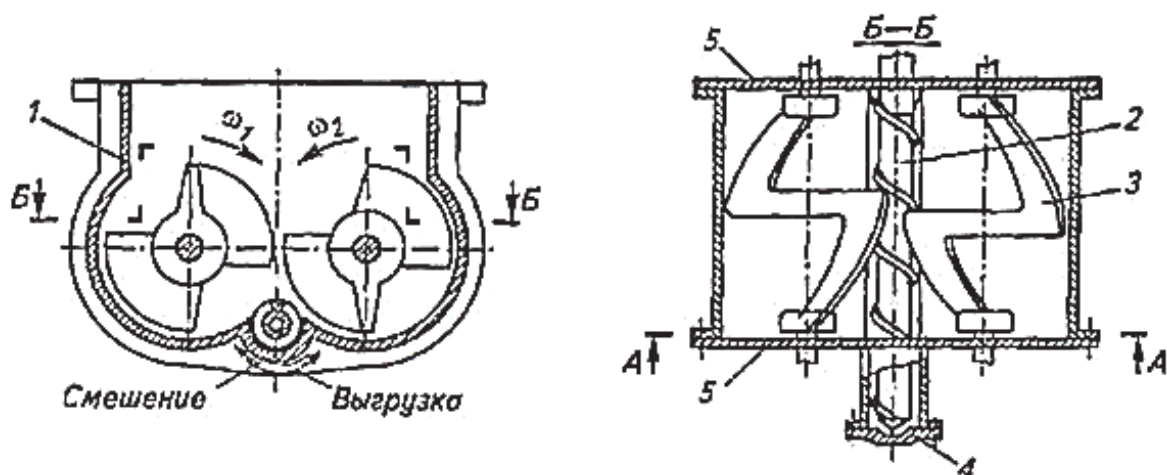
Двухроторный смеситель с реверсивным червяком
